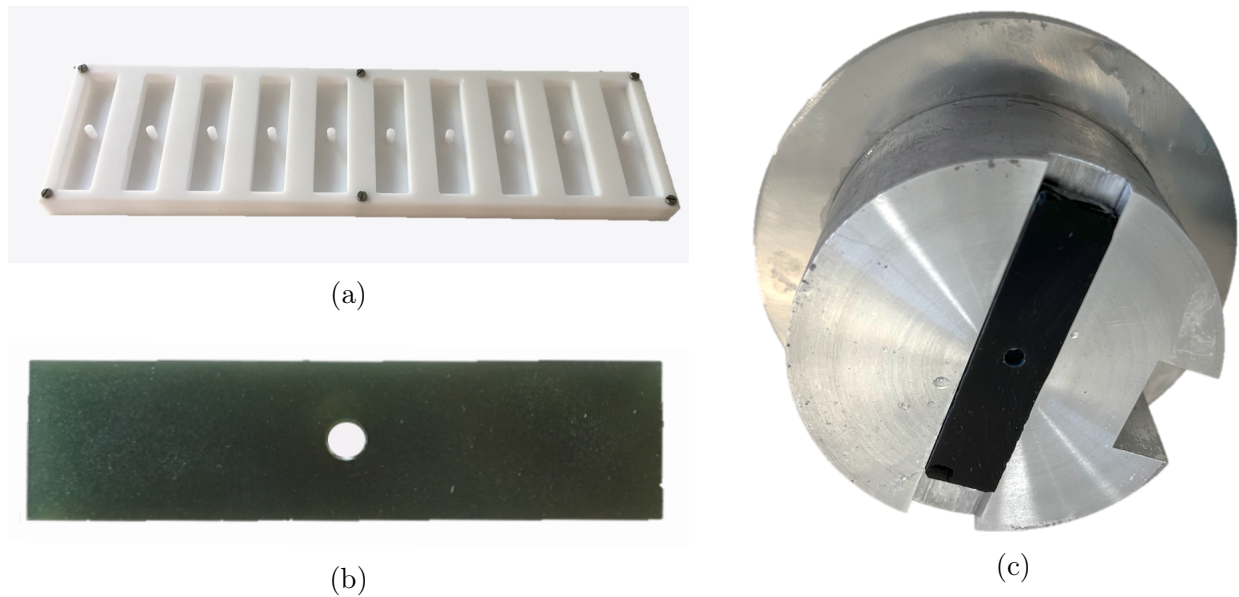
(a) Moule en PTFE pour la fabrication d'éprouvettes d'essais DCDC, (b) Éprouvette DCDC après polissage et (c) Outil permettant d'assurer le parallélisme des surfaces pendant le polissage.
